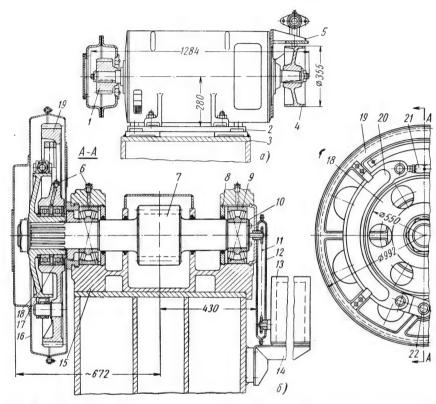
Электродвигатель (а) и промежуточный вал (б) напорного механизма
